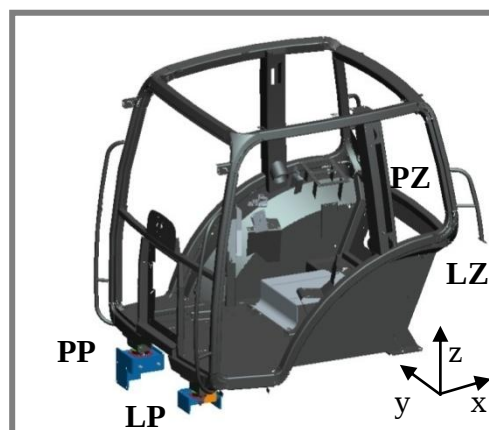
Detaily vybraných úchytných komponent [18]
